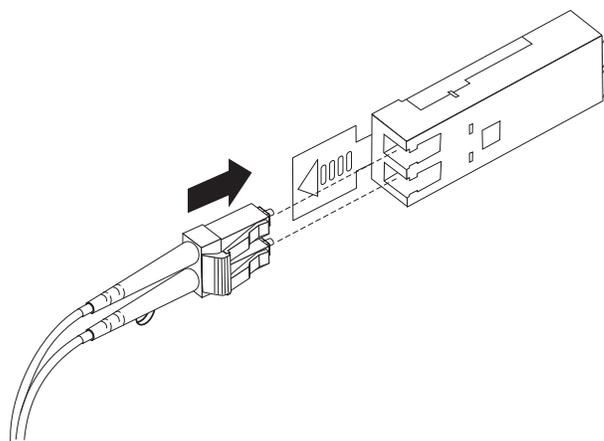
Inserindo um Cabo Fibre Channel LC-LC em um Módulo SFP
